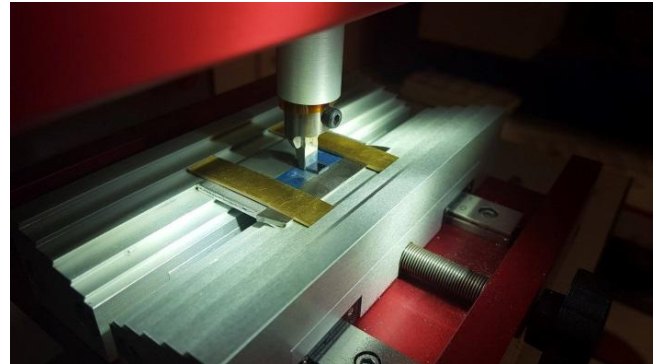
banc de test pour la résistance mécanique des soudures (cisaillement)
